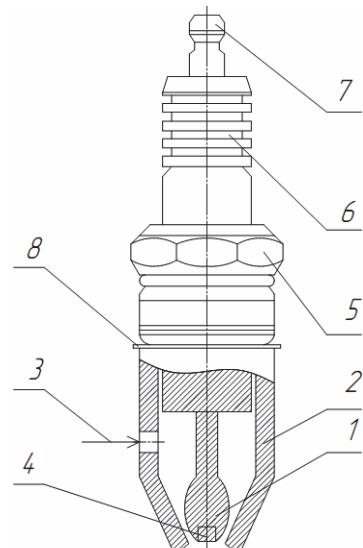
Схема плазмотрона постоянного тока: 1 – катод; 2 – анод; 3 – подача плазмообразующего воздуха; 4 – термоэмиссионная вставка; 5 – корпус; 6 – оребрение изолятора; 7 – контактная гайка; 8 – уплотнительное кольцо
